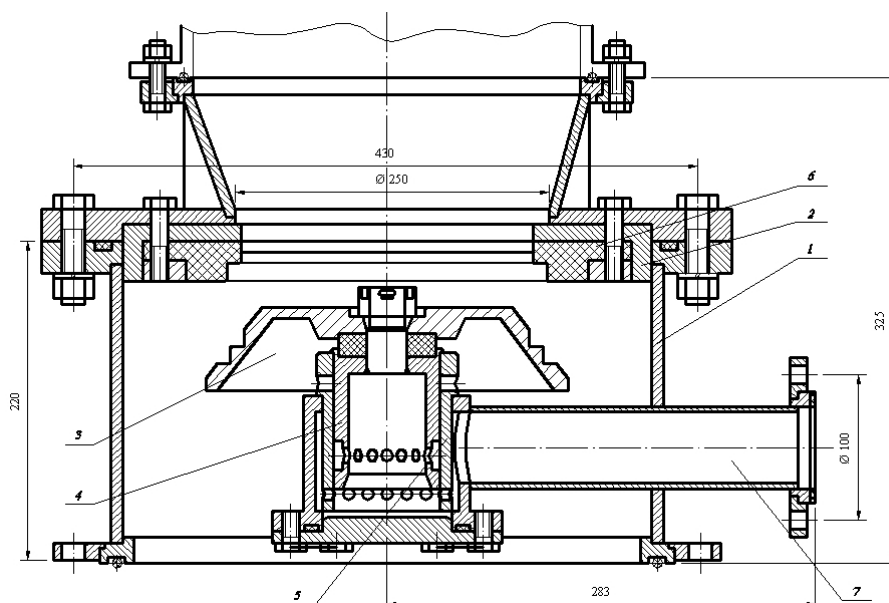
Конструкция модернизированного загрузочного клапана:
